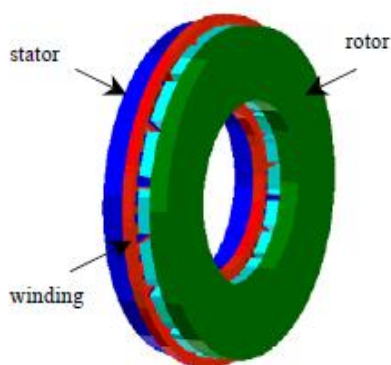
Croquis d'une machine à flux axial simple face (figure issue de [12]).
